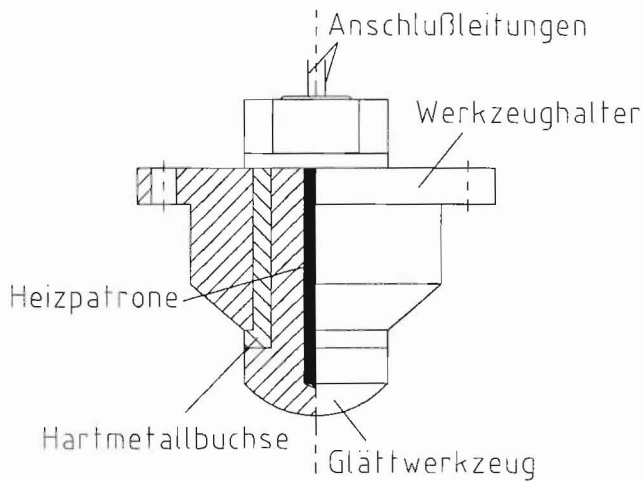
Aufnahmevorrichtung für elektrisch beheizte Werkzeuge zum Fixglätten
